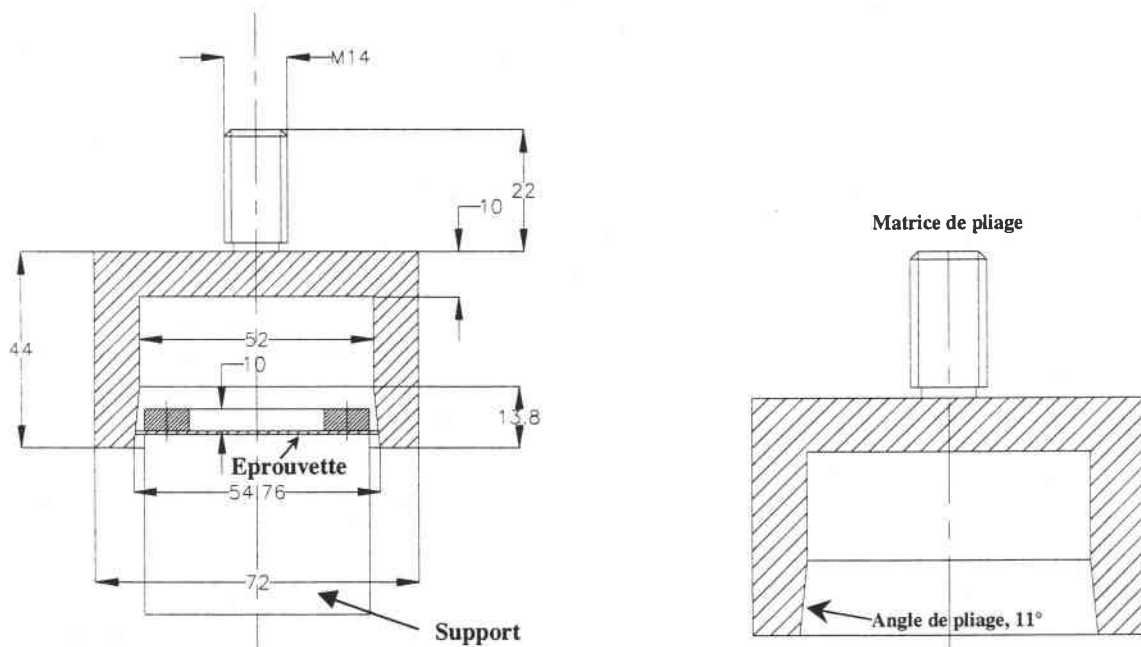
Définition du système mécanique défini pour le pliage des éprouvettes
